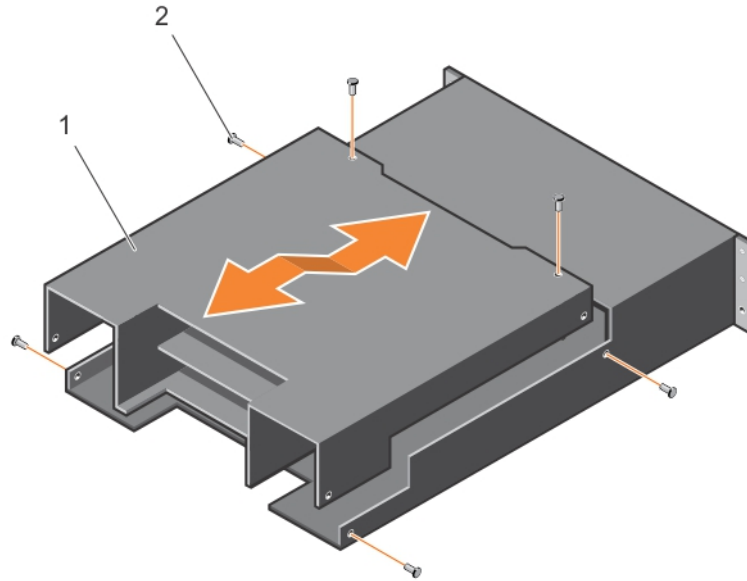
Entfernen und Installieren des EMM oder Netzteilgehäuses
